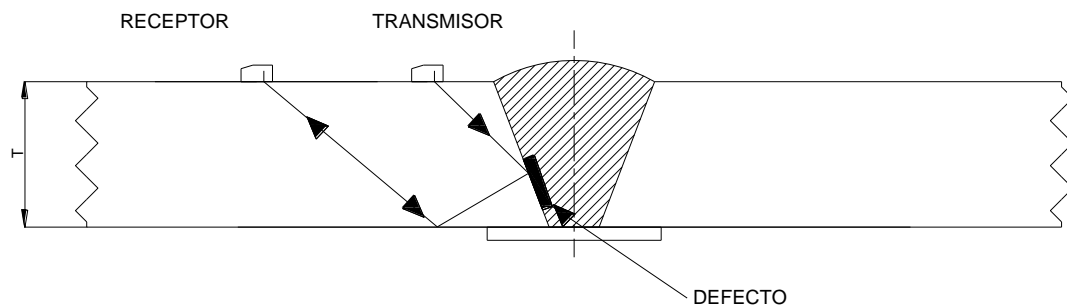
Utilización de sondas de onda transversal para localizar un defecto de una soldadura a tope.
